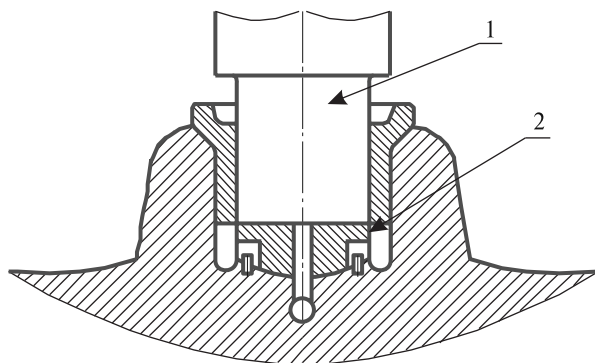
Опора вертикального вала: 1 — пята; 2 — подпятник
